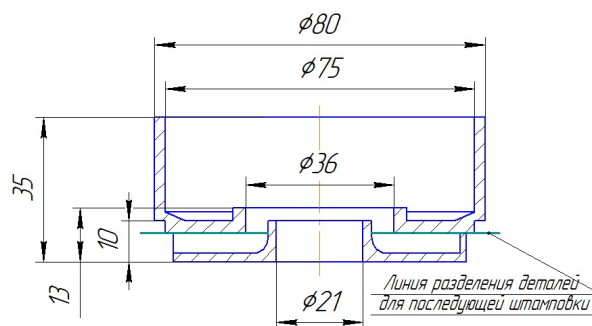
Схема разделения детали на 2 части для облегчения изотермической штамповки
